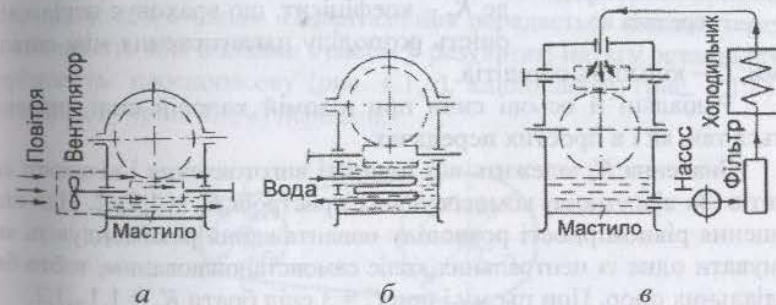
Схеми охолодження черв'ячного редуктора
